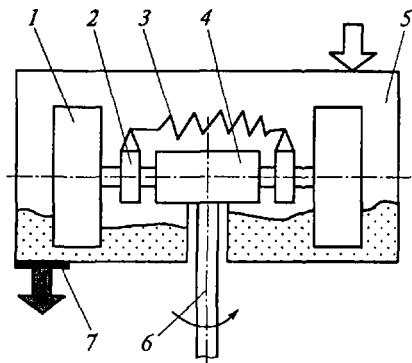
Катковый смеситель с неподвижной чашей:
